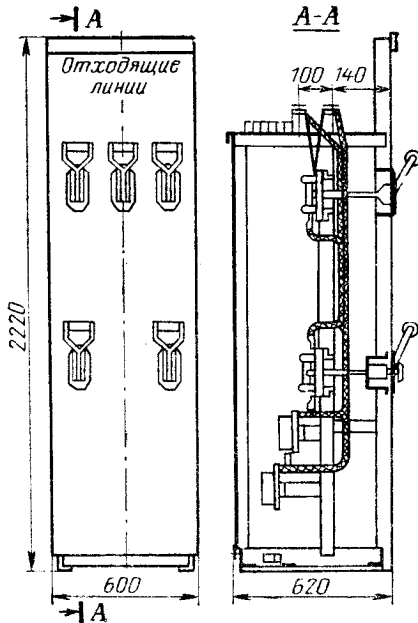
Общий вид и габариты панели ППН-05к-60.
